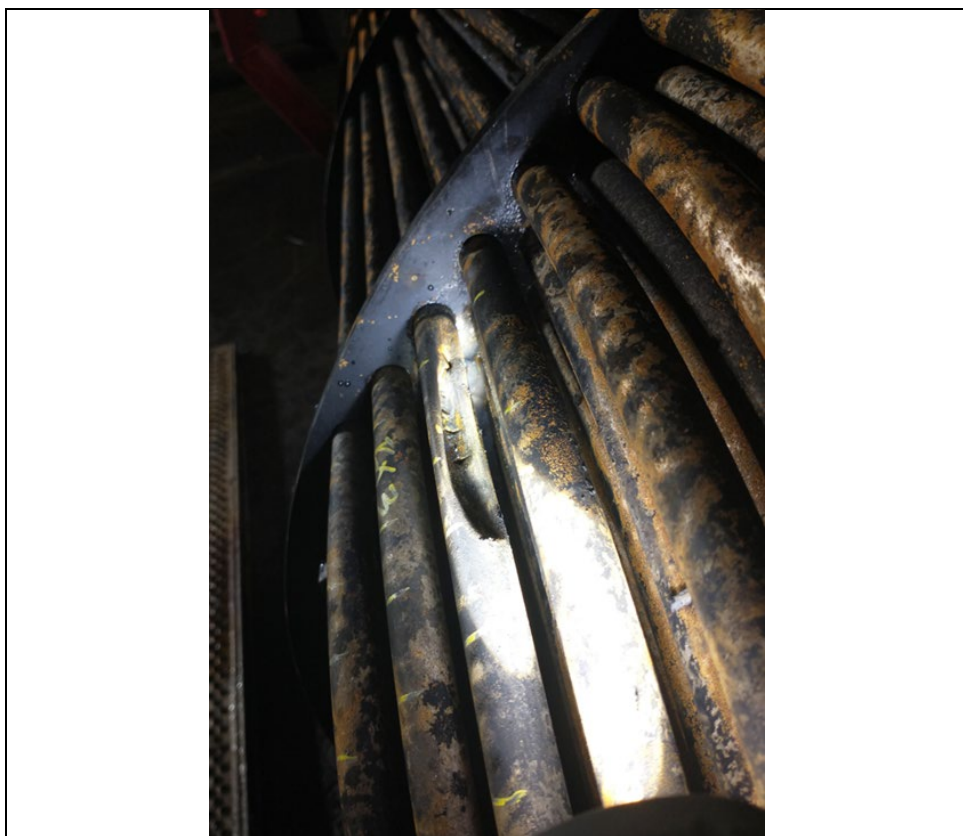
Mazo de tubos del 02-B donde se observa que un tubo colapsó debido al bajo espesor de pared y que la presión exterior del tubo es mayor a la presión interior. También se observan fisuras en la zona deformada debido a esta implosión.
